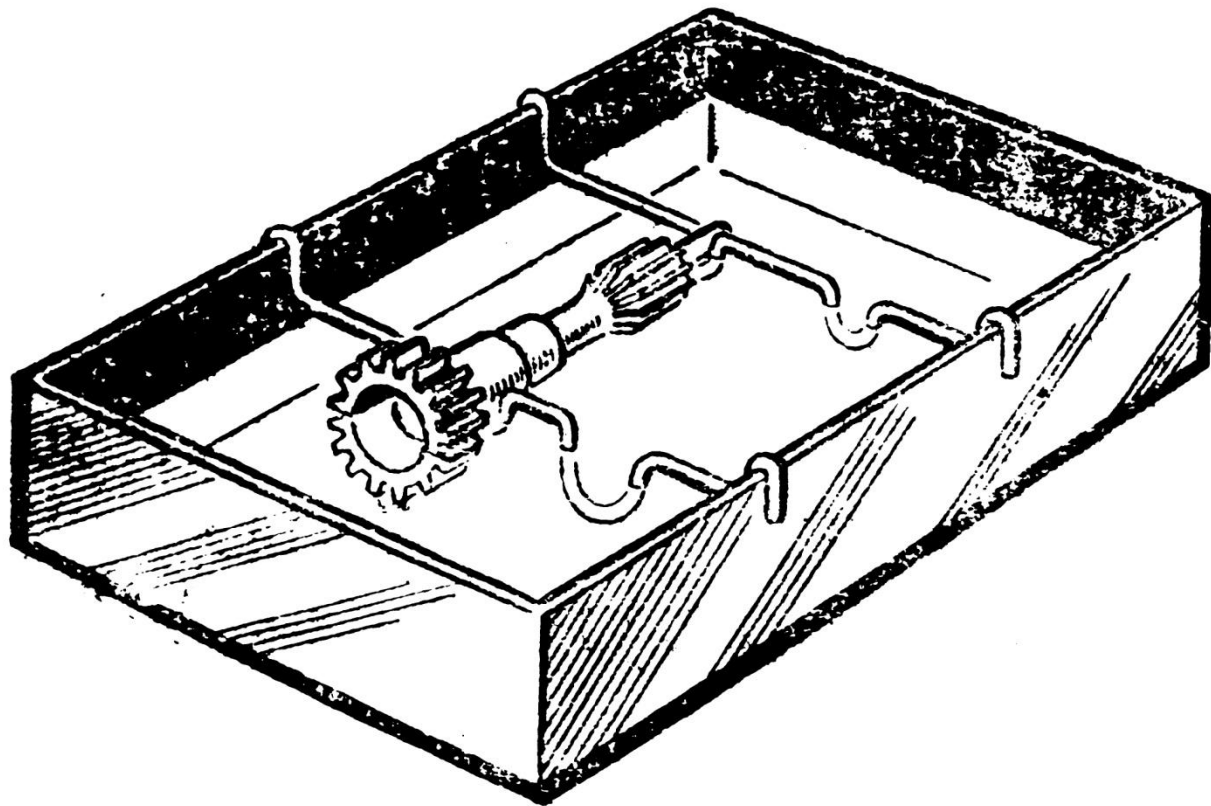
Положение ведущего вала коробки передач при наплавке зубьев сормайтом
